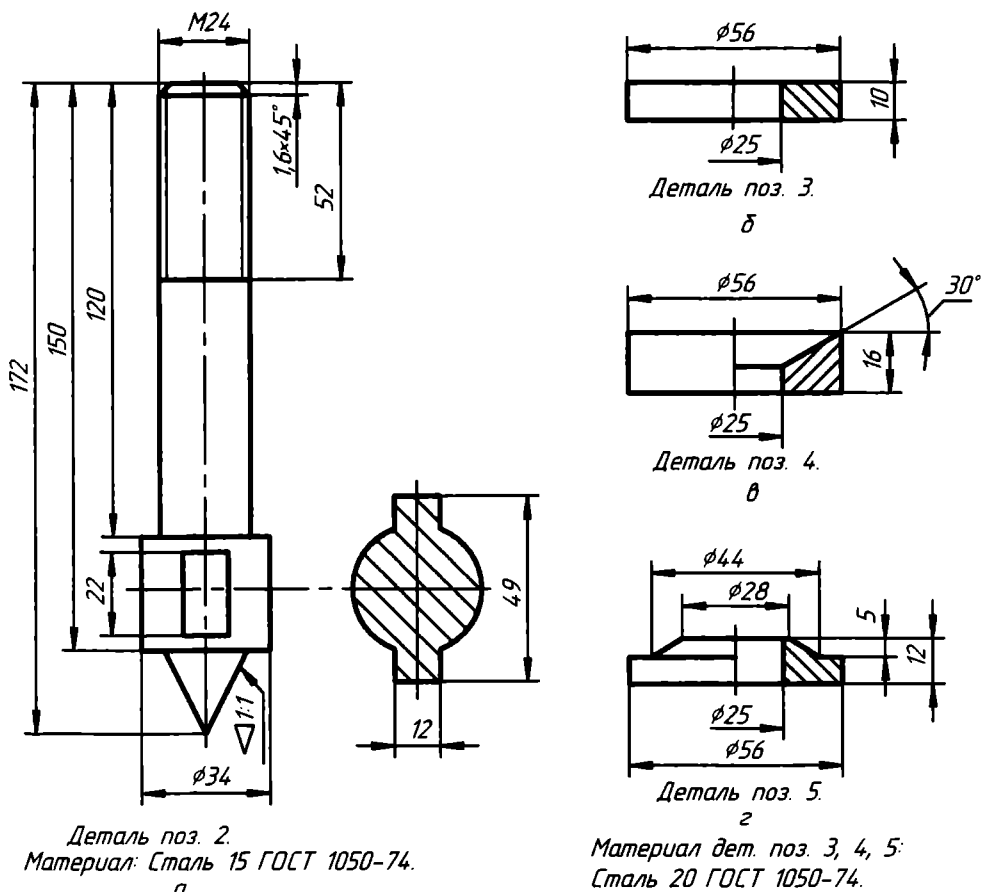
Чертежи: а — клапана; б — шайбы; в — опорного кольца; г — нажимного кольца
